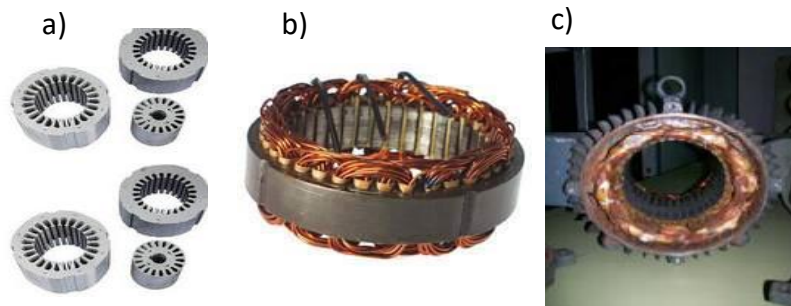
Estator del motor; a) Tipos, b) embobinado, y c) integrado a la carcasa.
